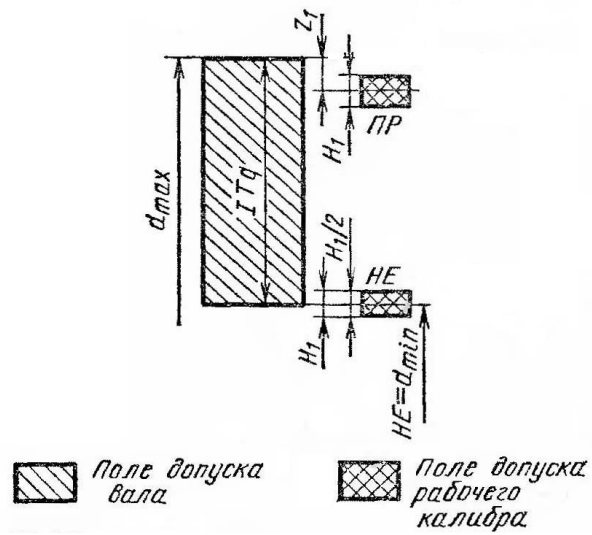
Схема расположения полей допусков вала и калибров.
